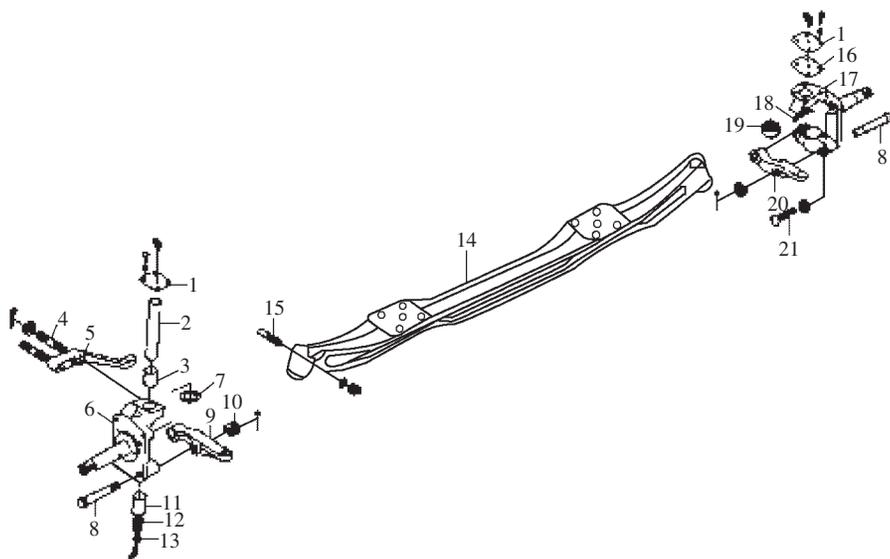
EQ1108G 型汽车前轴与转向节零件图
